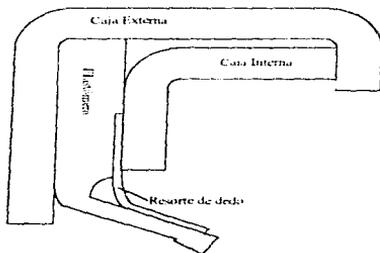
Diseño Básico de un Retén Ensamblado.
